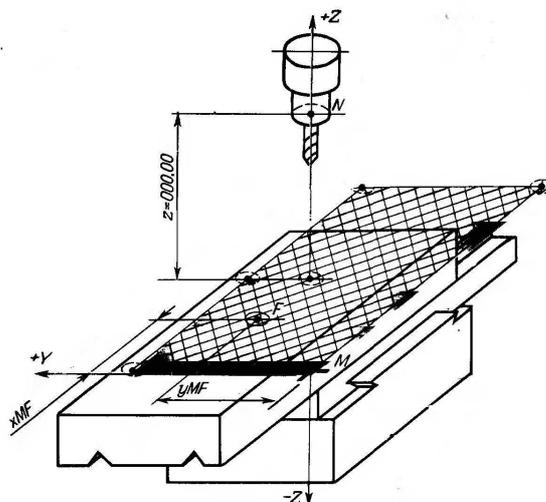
Система координат вертикального сверлильного или фрезерного станка
